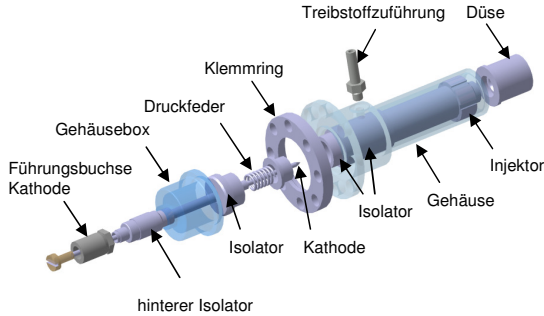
Explosionszeichnung des untersuchten Triebwerks
